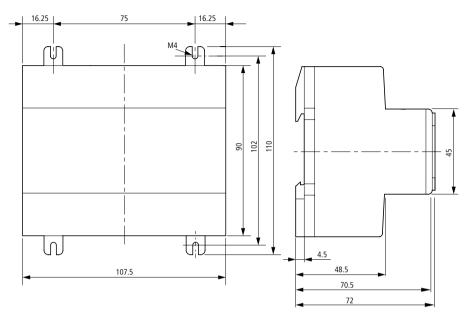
Dimensions des appareils easy800, en mm (indications en inches → Tableau 9)
